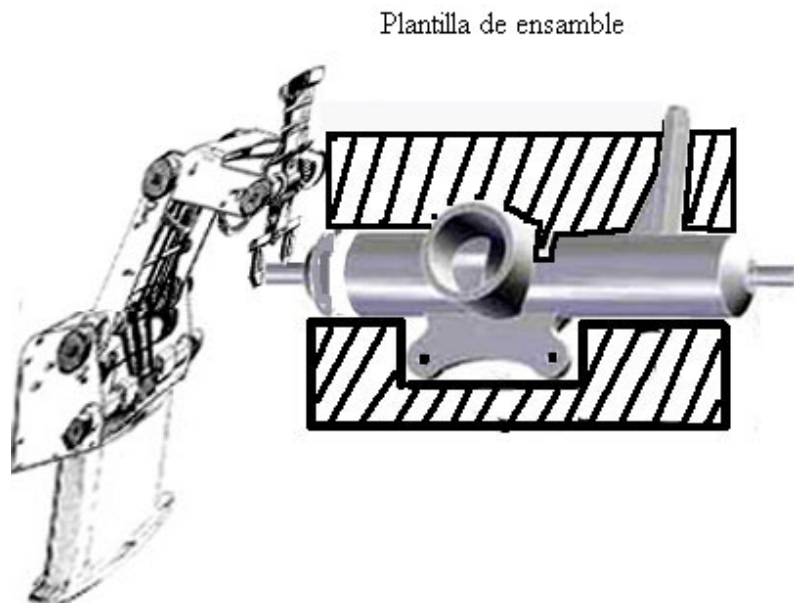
Plantilla de ensamble para fijar tolerancias geométricas.
